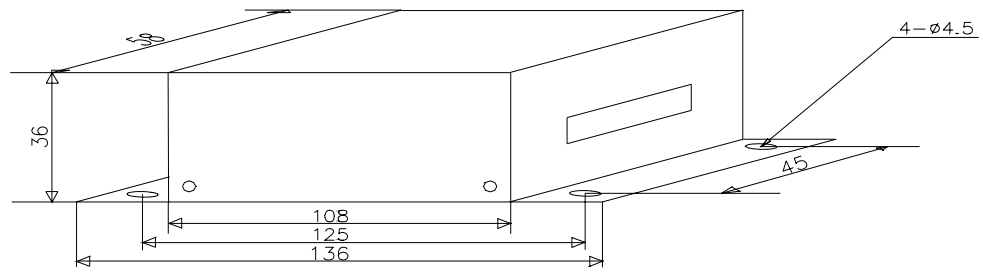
直流电压采样盒的外形尺寸和安装固定尺寸 (单位: mm)
